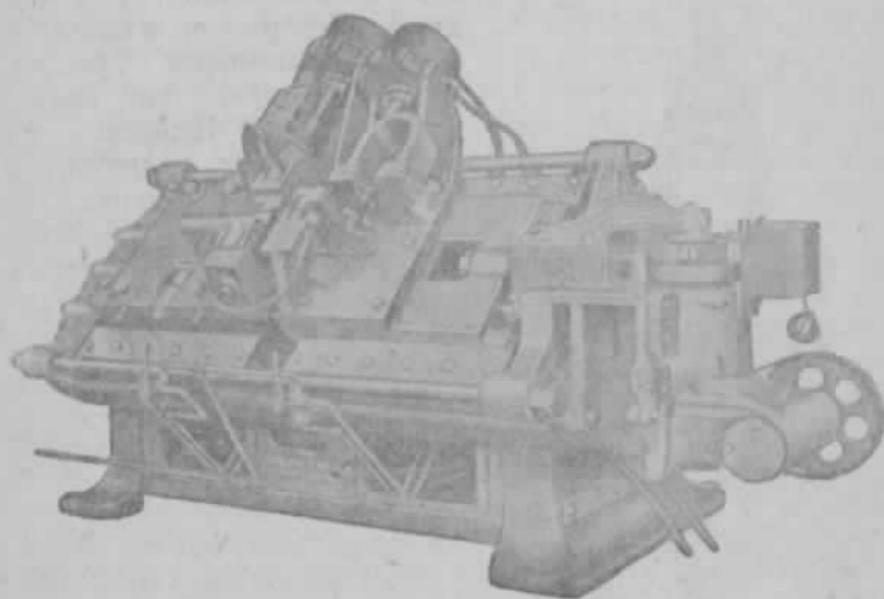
Сварочный станок по методу Томпсона.
